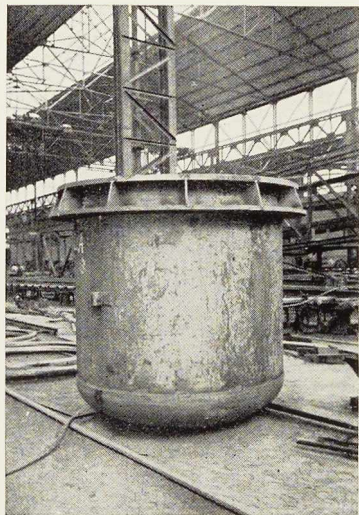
Montage et pointage des brides avant soudage, la cuve étant placée sur son fond.
